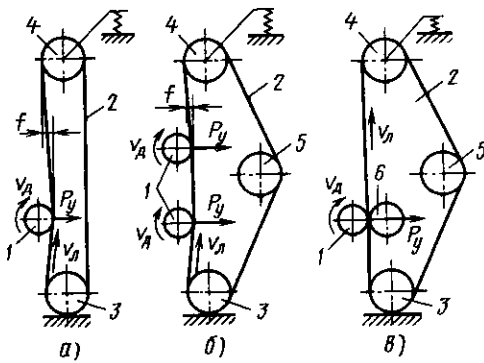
Схемы обработки бесконечными лентами: а — на свободной ветви ленты; б — на свободной ветви ленты с опорным роликом; в — с поджатием ленты к обрабатываемой поверхности заготовки при помощи контактного ролика; 1 — обрабатываемая заготовка; 2 — лента; 3 — приводной ролик; 4 — натяжной ролик; 5 — опорный ролик; 6 — контактный ролик
